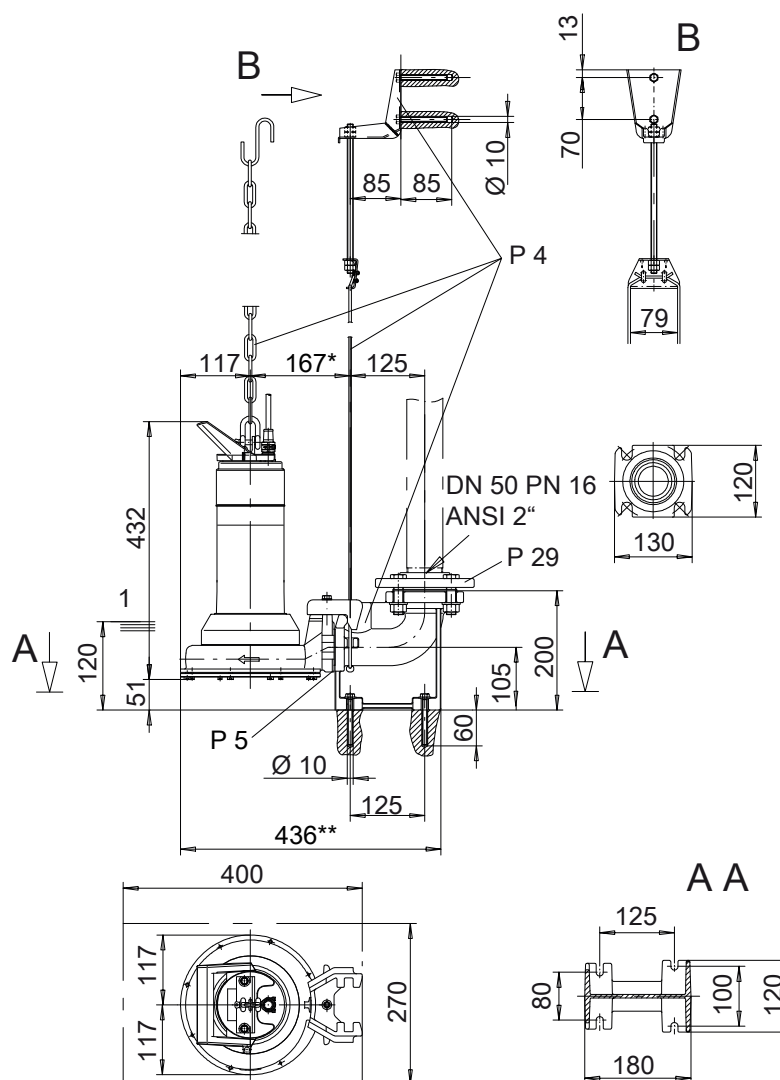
Maßzeichnung Ama-Drainer 522 ND/11 mit Führungsseil
